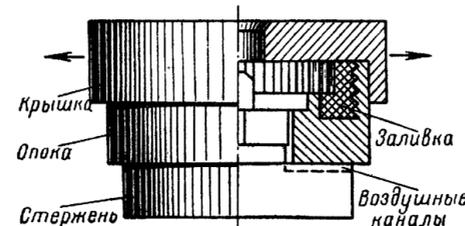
Пресс-форма для изготовления цилиндрических зубчатых колес
